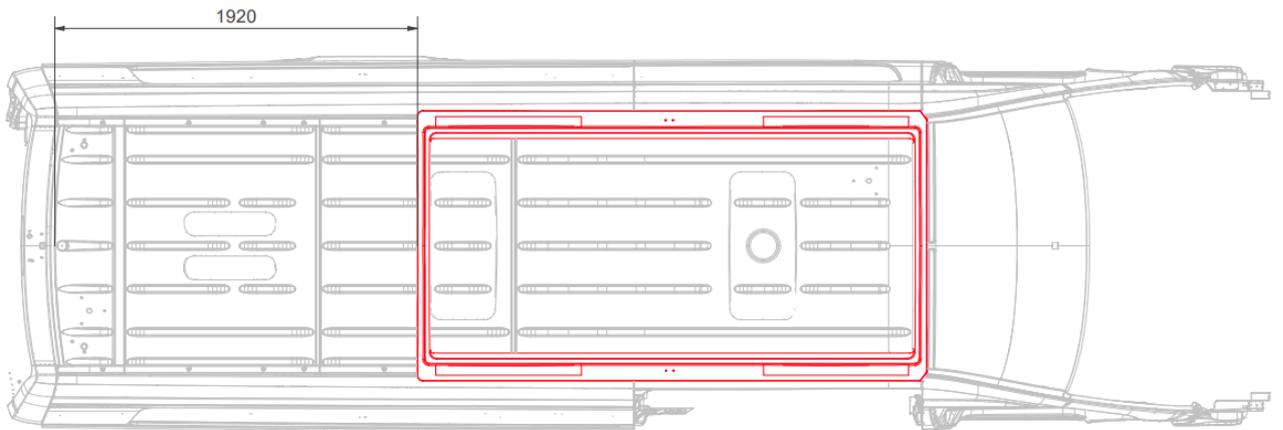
MB Sprinter L3H2 (L = 7367 mm) [G0002136]
